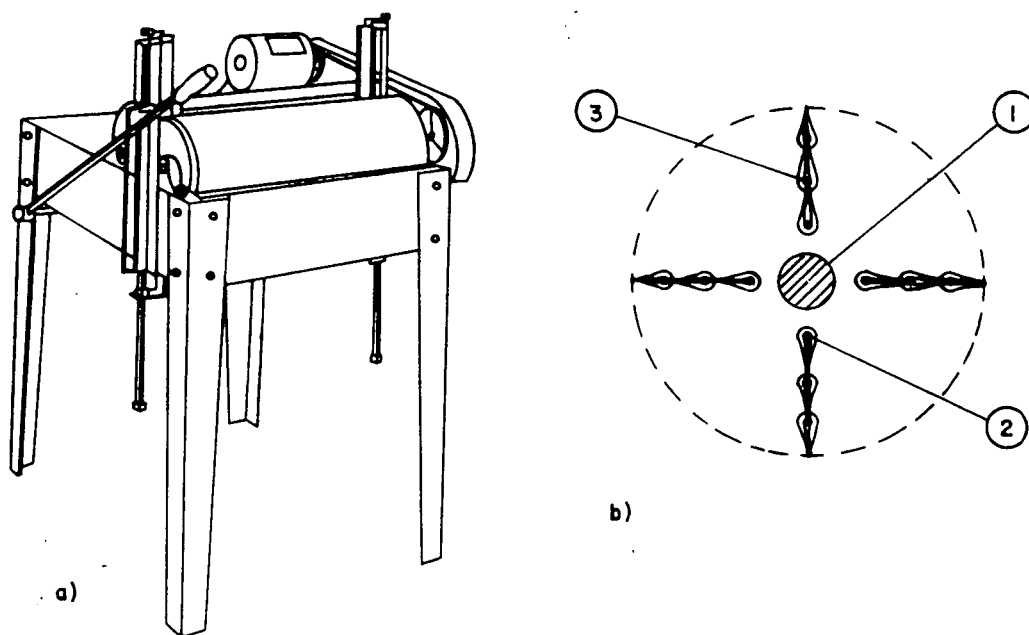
a) Máquina desoperculadora com correntes giratórias [14]. b) Desenho esquemático do rotor de corte.
